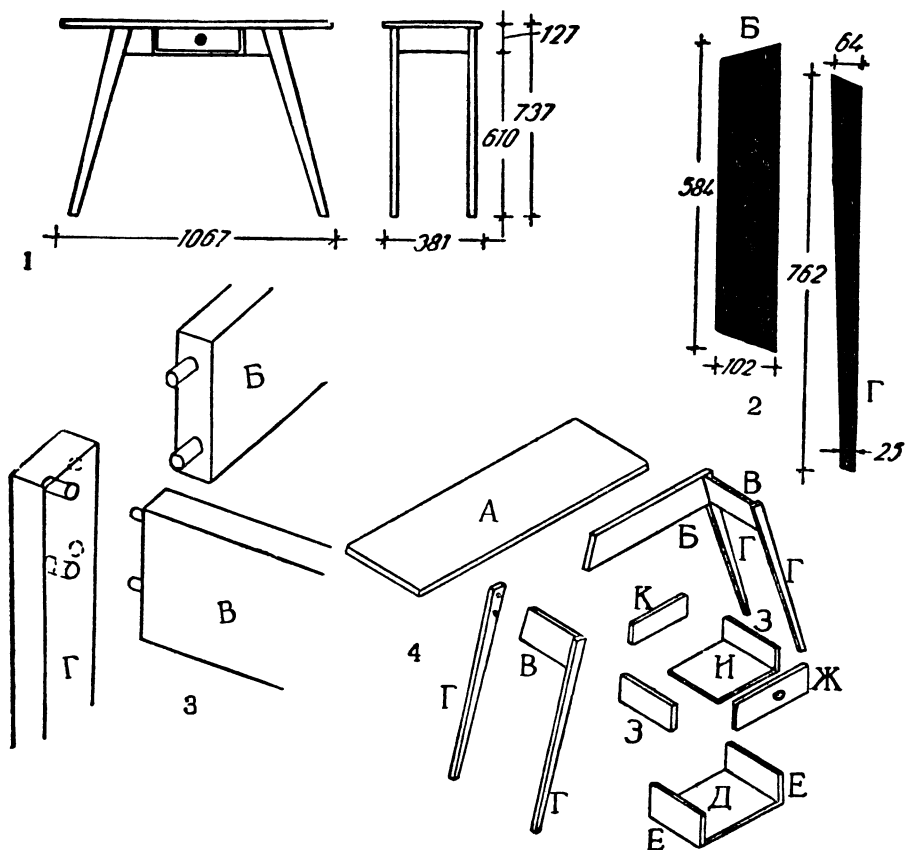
4. 1 — вид спереди и сбоку; 2 — детали царги и ножки; 3 — эскиз соединения ножки с царгами; 4 — эскиз сборки деталей.
